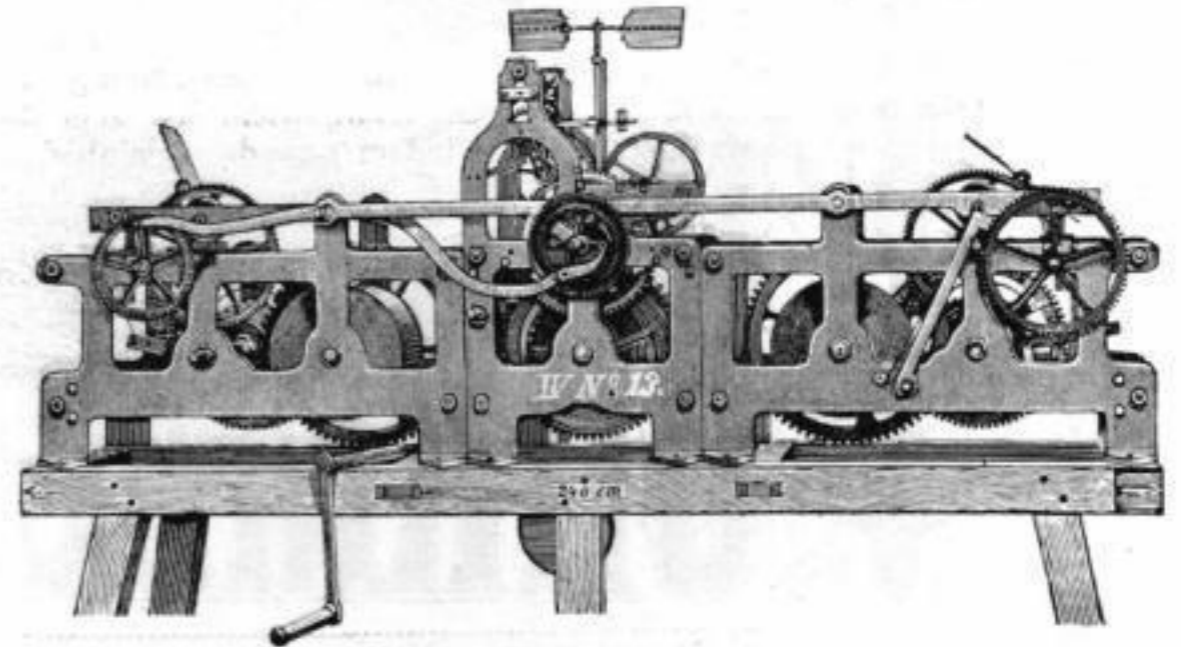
Ansicht der Uhr. Nach einem Aufzuge 8 Tage gehend. Mit constanter Kraft. Viertel- und Stunden-Schlagwerk.
